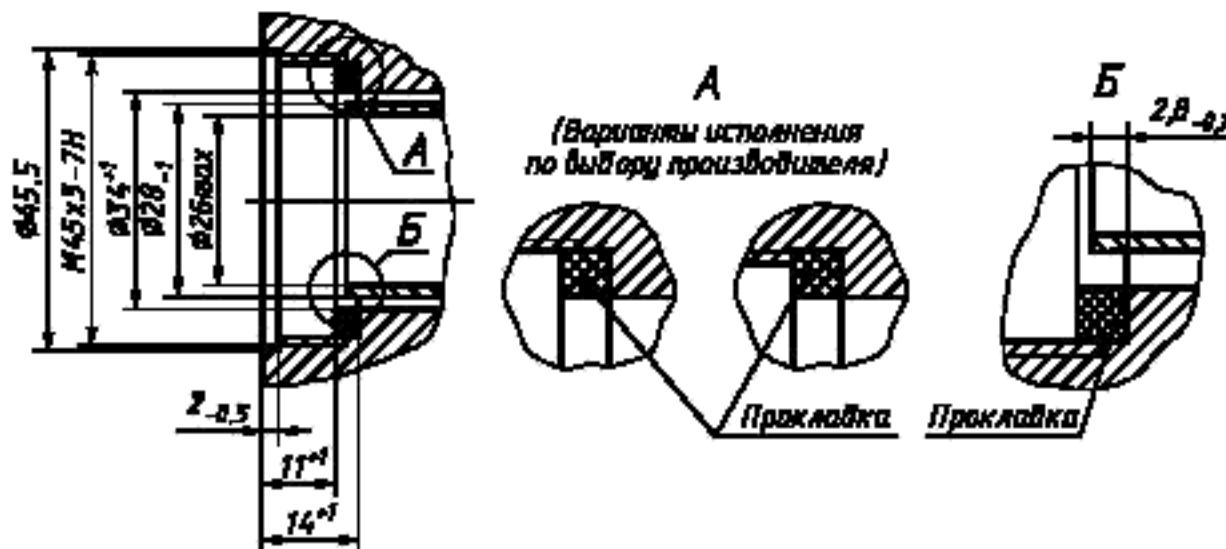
Резьбовое соединение с внутренней резьбой для систем с двумя каналами подачи воздуха РIV
